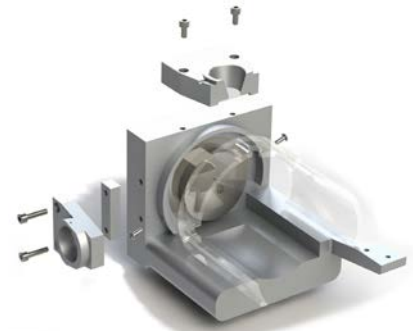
Thermo Fisher Flex Ion Source ES071 mit Montagekit (Explosionsansicht)
